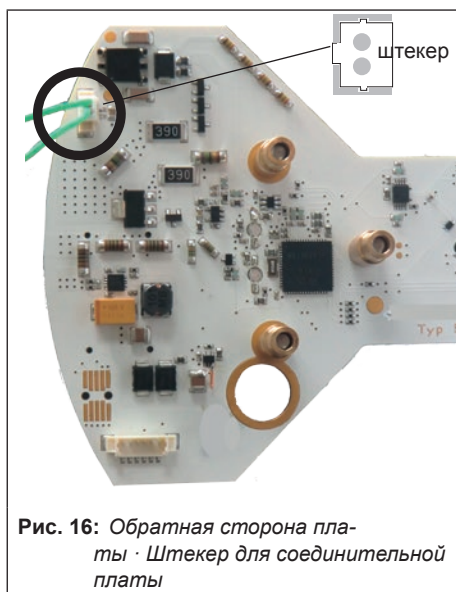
Обратная сторона платы · Штекер для соединительной платы
